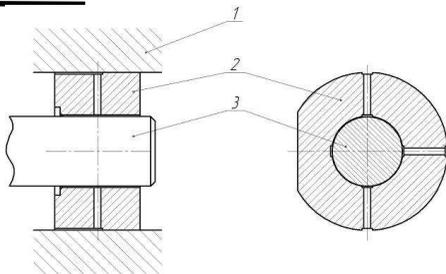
ГСДП2: 1 – корпус насоса; 2 - подшипник; 3 – цапфа вала
